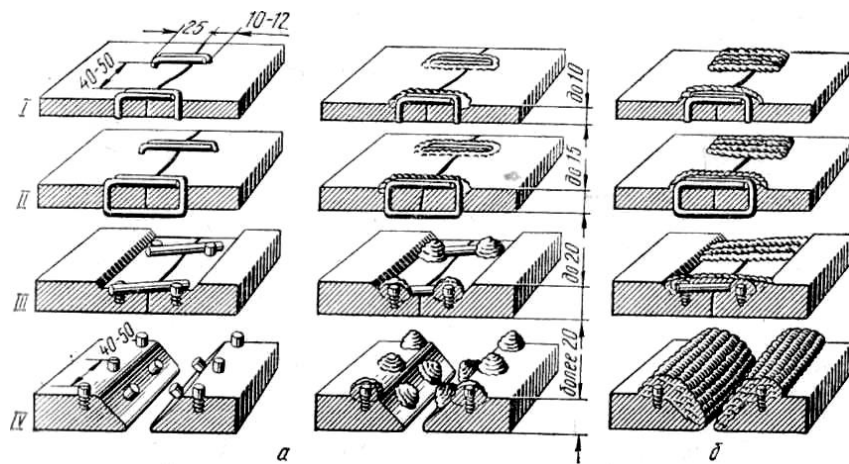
Зварювання чавунних деталей з постановкою штифтів і скоб: підготовка і початок обварки; б - подальше і остаточне зварювання; I, II - зварювання з постановкою скоб; III, IV - зварювання з постановкою різьбових штифтів.
